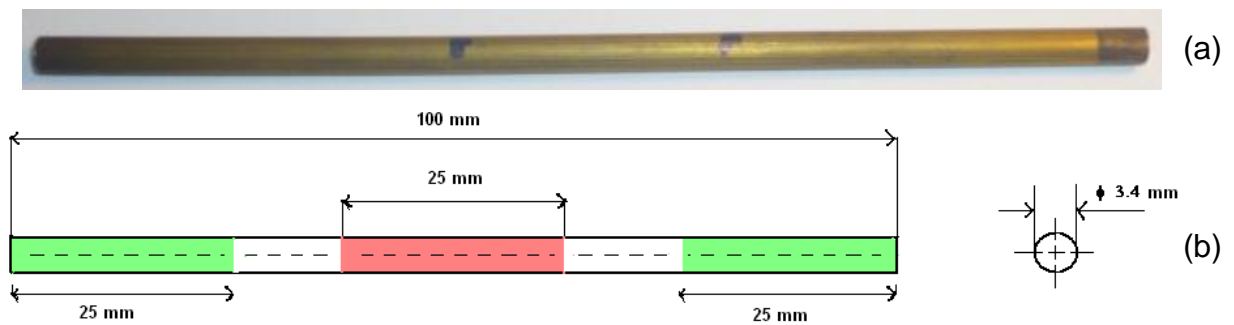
Geometría de la probeta de tracción. a) probeta de CuAlBe, b) zona dentro de la probeta de tracción.
